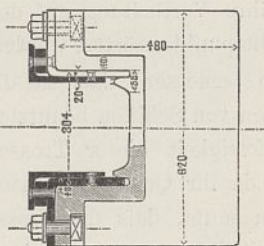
Grundriss und wagenrechter Schnitt.
